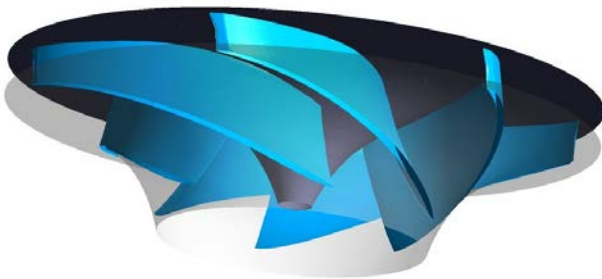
3D-модель робочого колеса оборотної гідромашини
